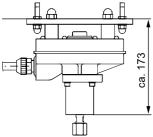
Dessin coté du régulateur de vide sur la plaque de fixation
